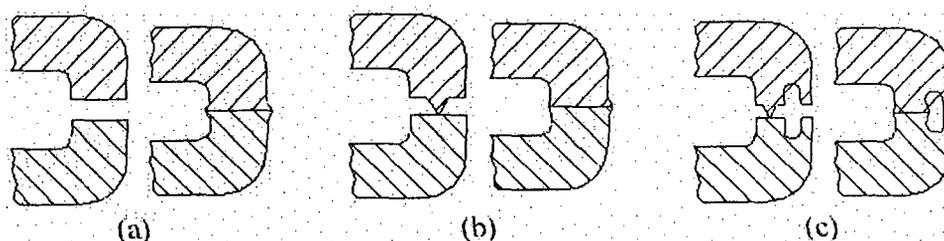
Uniões planas para soldagem ultrasônica.
